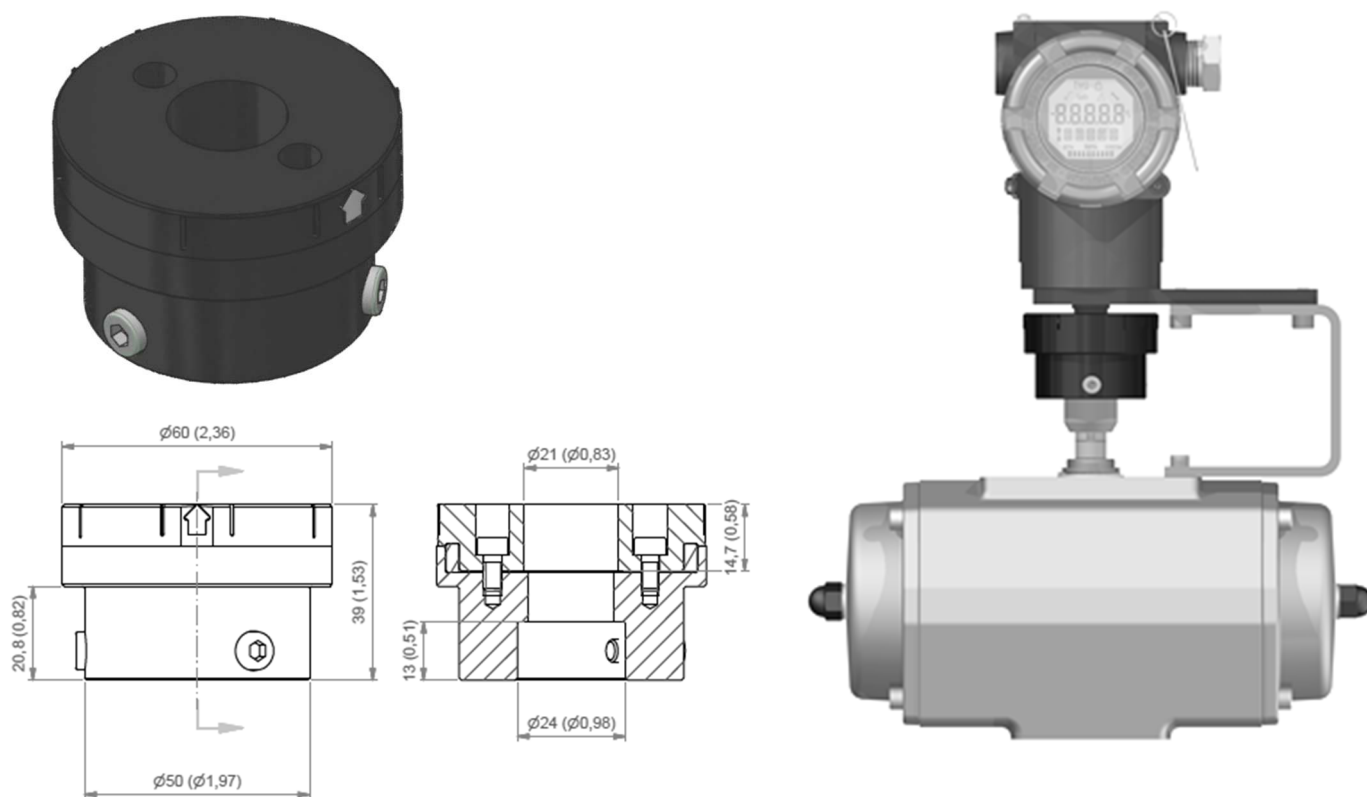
Dimensional e montagem do ímã rotativo.
